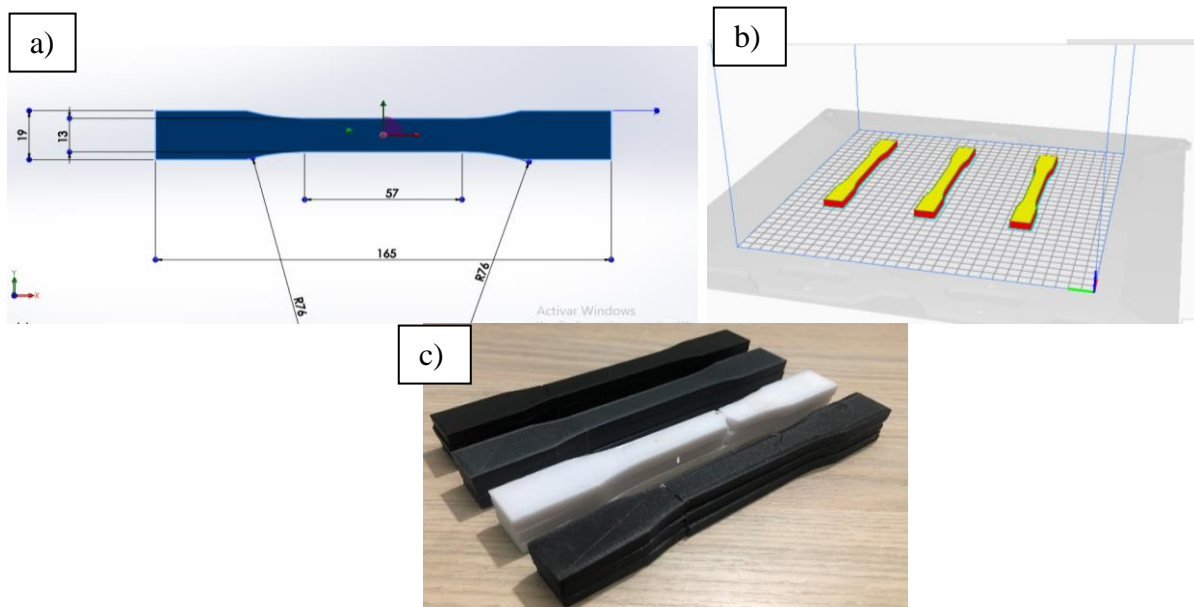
a) Diseño CAD probeta para ensayo de tensión. b) Diseño en programa Cura, formato STL, c) probetas tensión impresas en 3D PLA, PLA+F.C., PETF y PETG+F.C. fuente: Autor.
